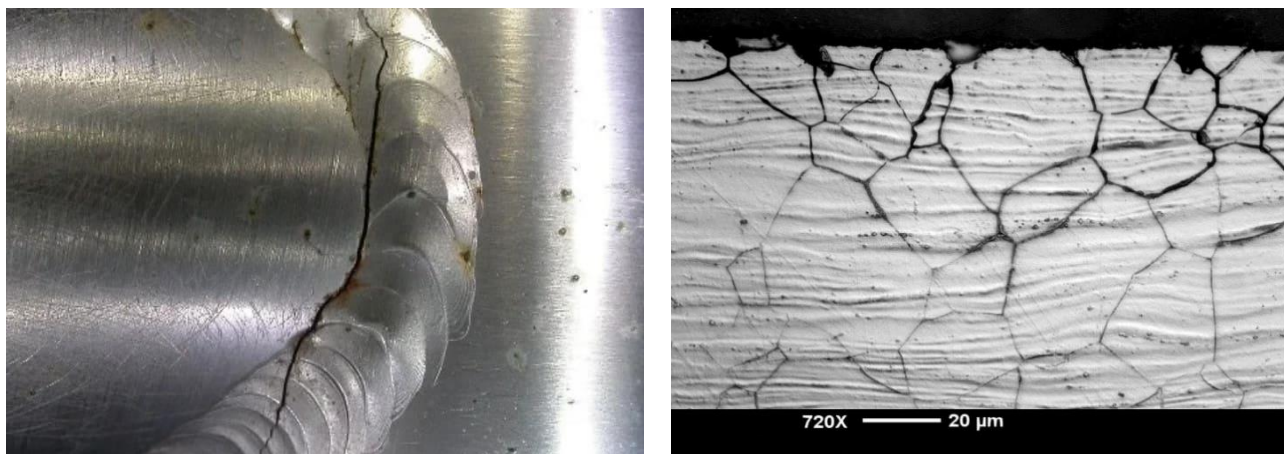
Горячая трещина и межкристаллитная коррозия сварного шва
